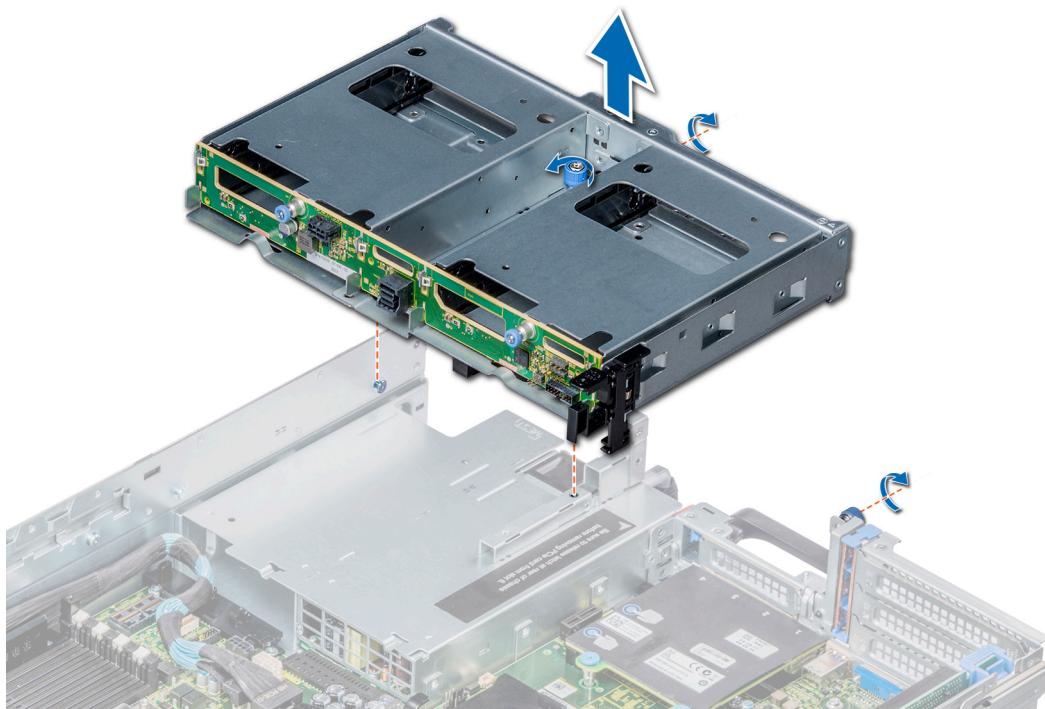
Entfernen eines hinteren Gehäuses mit zwei 3,5-Zoll-Festplatten
